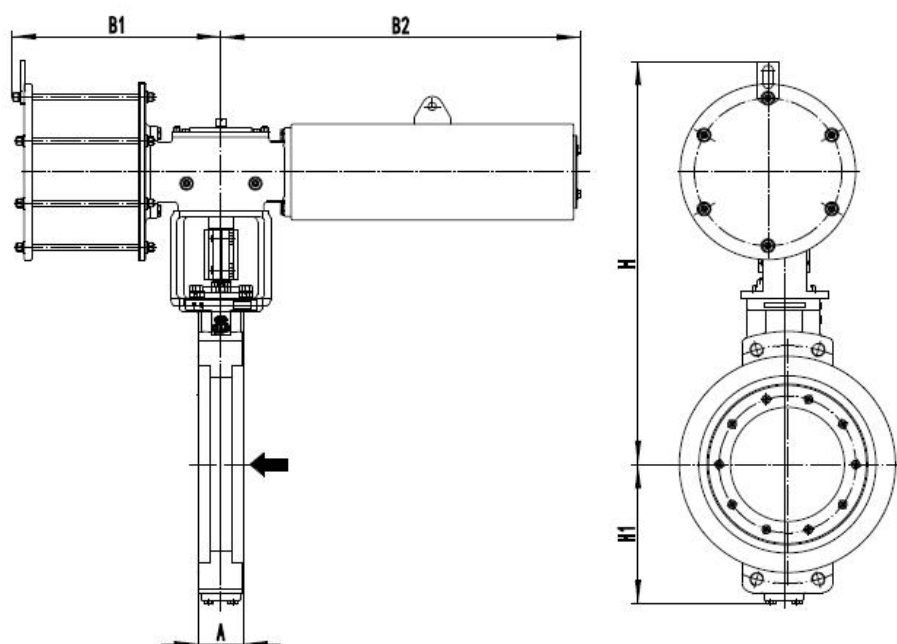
配 AW18SR41~AW85SR56 外形尺寸图 (FC)
